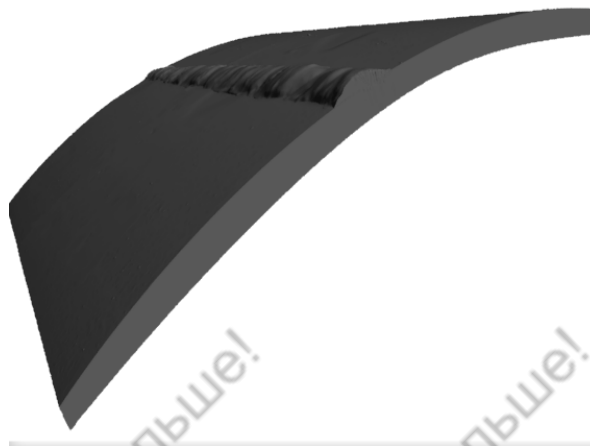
ПРИМЕР продольного сварного стыкового соединения
